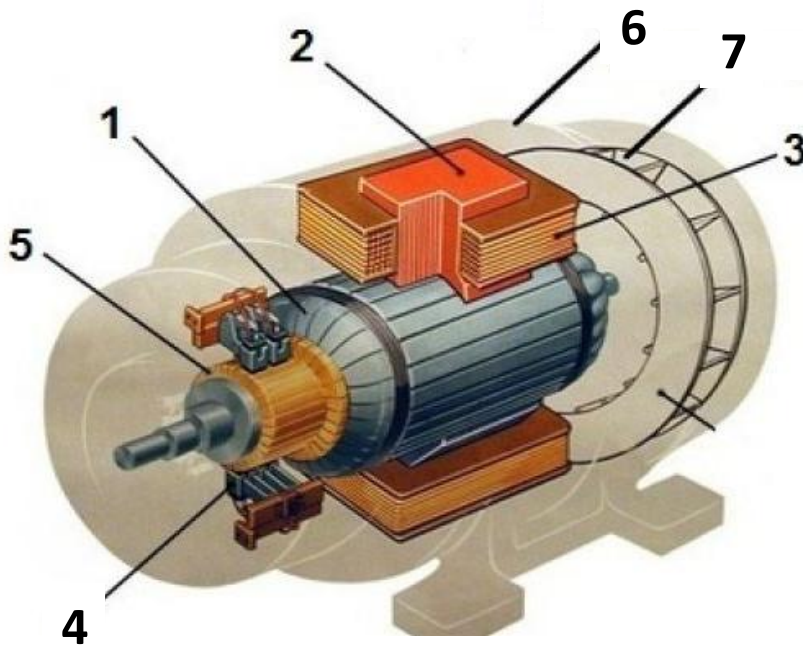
Конструкція синхронного двигуна: 1–якір; 2–сердечник полюса; 3–обмотка полюса; 4–щітки; 5–колектор; 6–корпус; 7–вентилятор.
